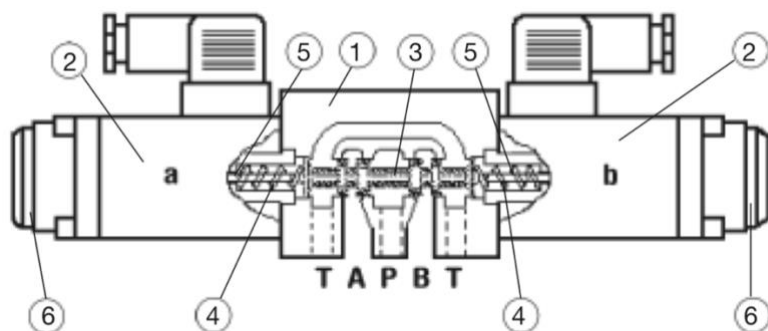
Sähköohjattu 4/2 suuntaventtiili. (Pippo Hydraulic)
